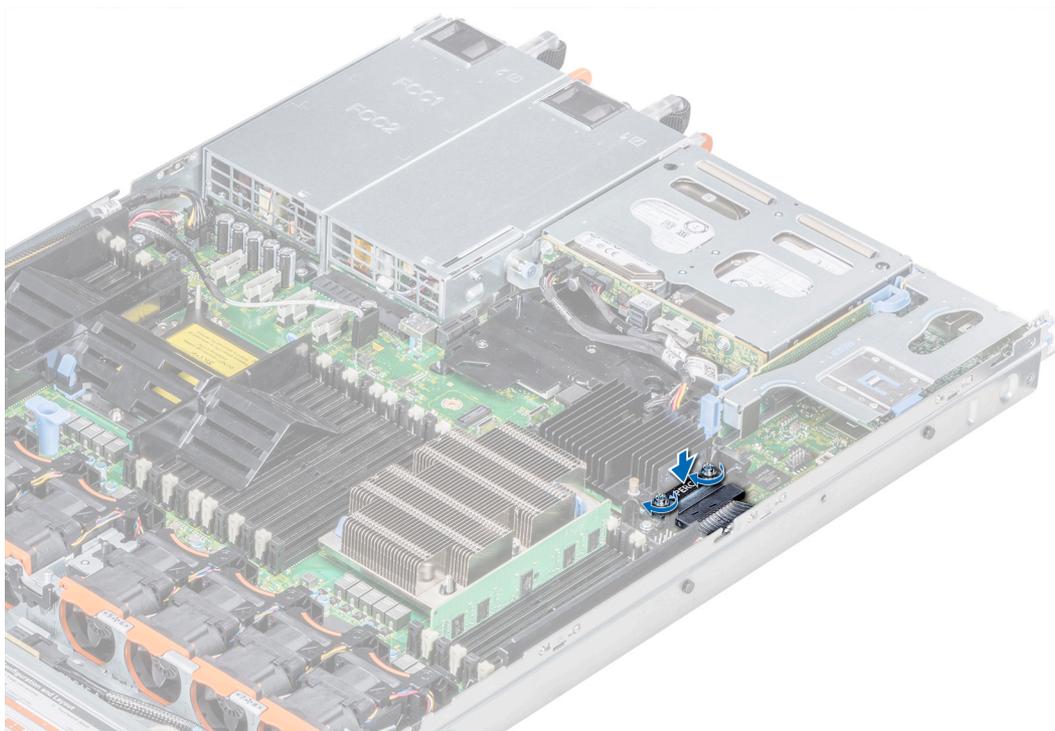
Instalación del cable de la tarjeta controladora de almacenamiento integrada
